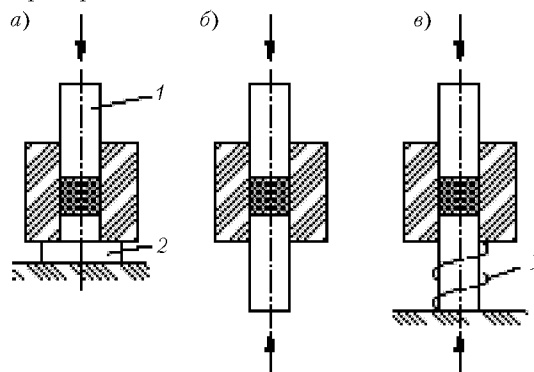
Схемы таблетирования: а — одностороннее; б — двустороннее; в — с «плавающей» матрицей; 1 — верхний пуансон; 2 — нижний пуансон; 3 — пружина
